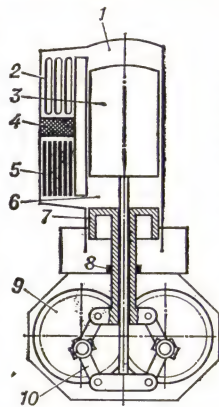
Схема двигателя внешнего сгорания: 1 — горячая полость; 2 — нагреватель; 3 — поршень-вытеснитель; 4 — регенератор; 5 — охладитель; 6 — холодная полость; 7 — рабочий поршень; 8 — наружное уплотнение; 9 — зубчатые колёса, синхронизирующие работу поршней; 10 — ромбический механизм.
